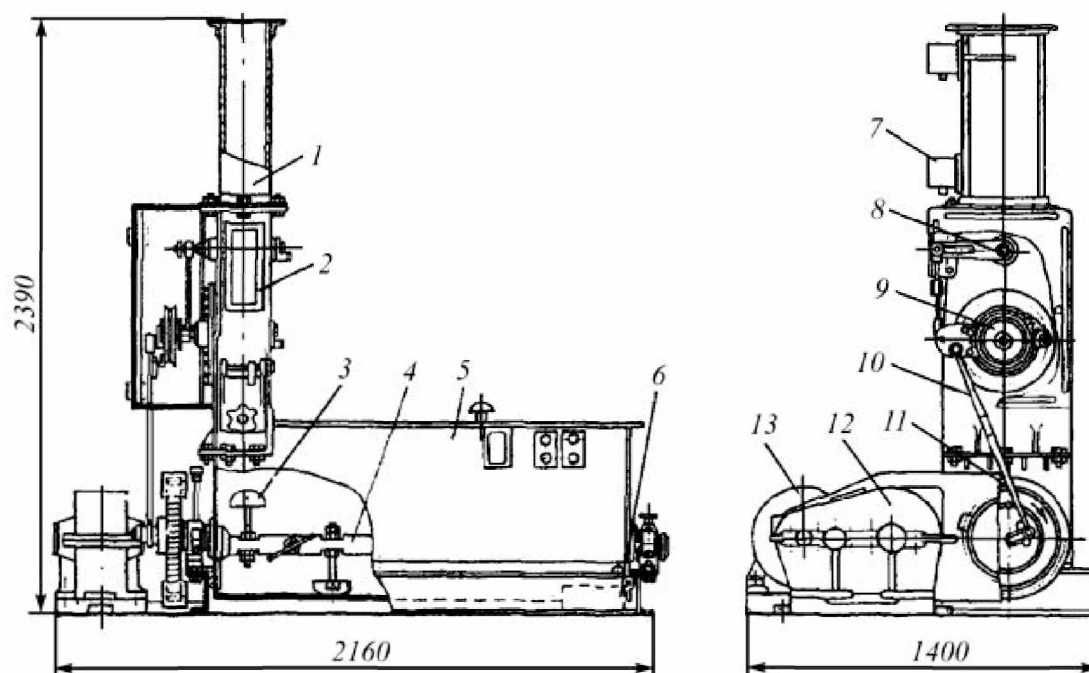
Тістомісильна машина Х-12Д: 1 – патрубок борошна; роторний дозатор борошна; 3 – місильна лопать; 4 – місильний вал; 5 – робоча камера; 6 – станина; 7 — датчик рівня; 8 – зворушувач; 9 – храповик; 10 – кривошипно-шатунний механізм; 11 – зубчаста передача, 12 – редуктор; 13 – електродвигун.
